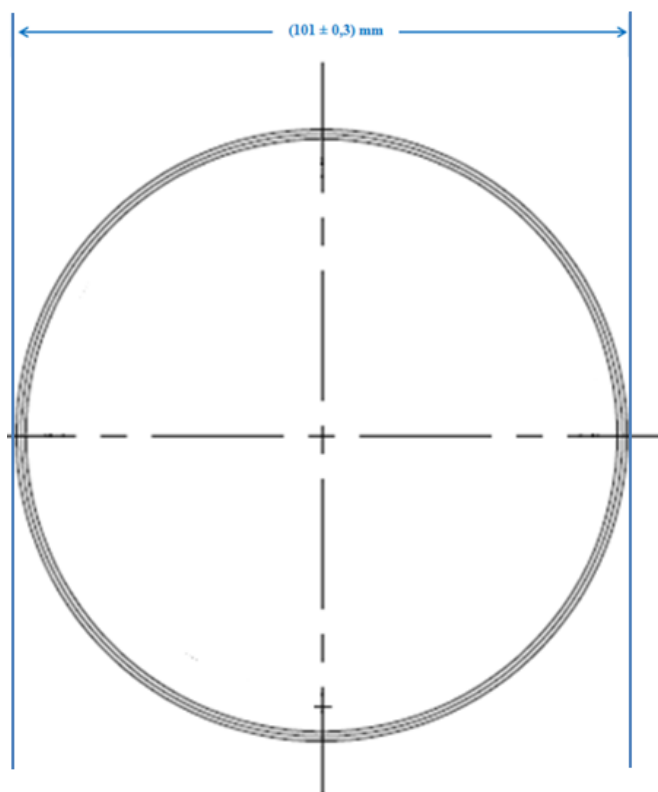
Dimensionamiento de la sobretapa, vista frontal.
